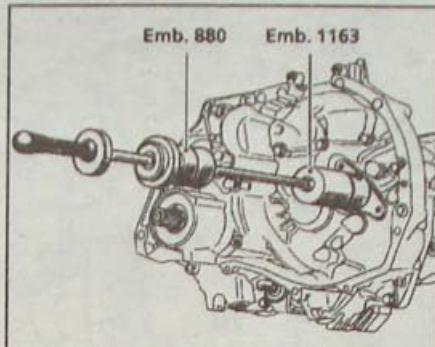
Использование съемника Emb. 880 и приспособления Emb. 1163 для снятия направляющей втулки подшипника выключения сцепления
